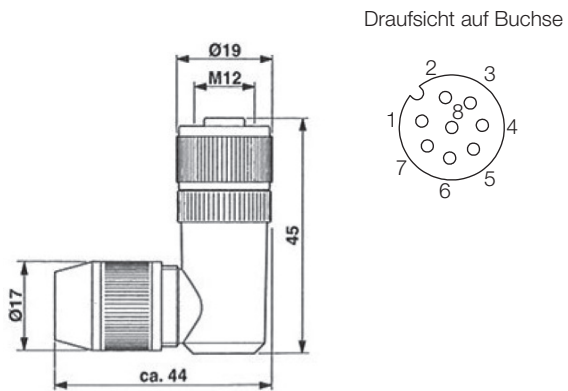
Steckverbinder BCC M488-0000-1A-000-43x834-000
